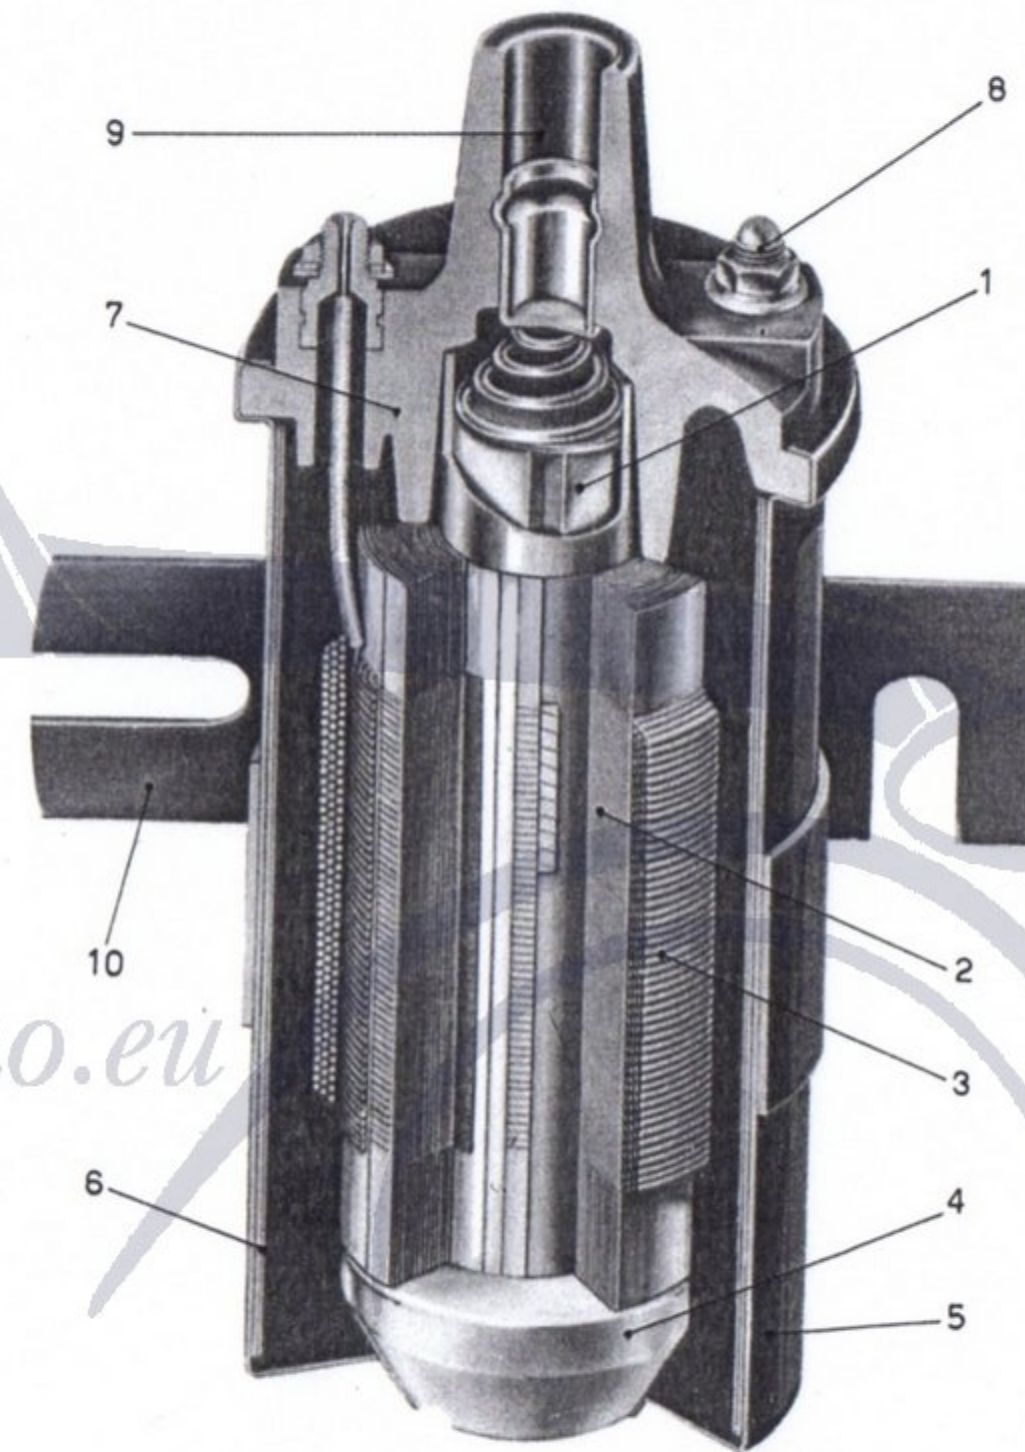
Sezione di una bobina d'accensione Magneti Marelli per autoveicoli con motore a quattro o a sei cilindri.
